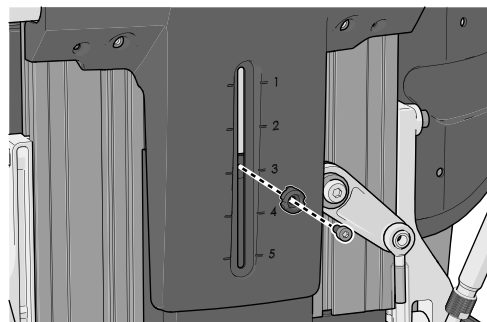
Der Kunststoffknopf ist mit einer Schraube befestigt.
